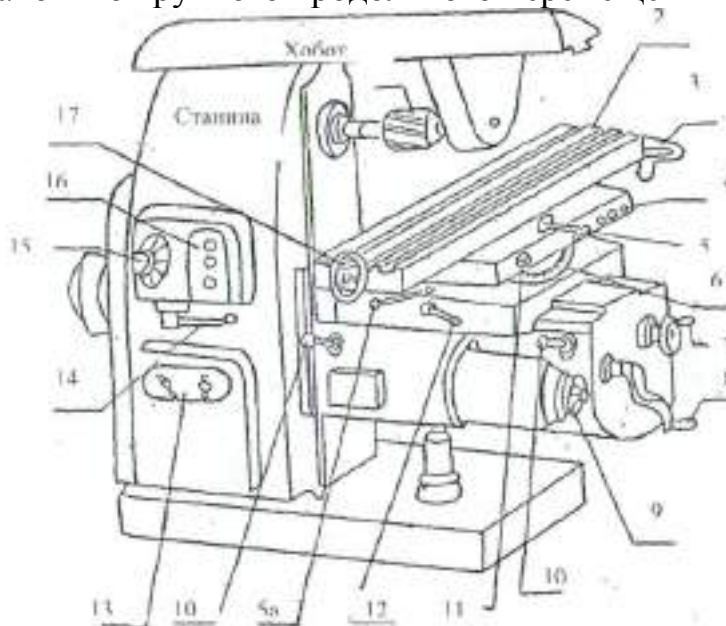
Общий вид универсального горизонтально-фрезерного станка
